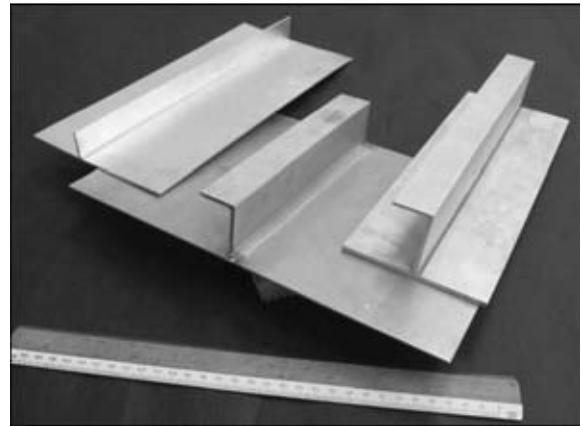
Фрагменты тонколистовых стрингерных панелей, изготовленных с выполнением электронно-лучевой сварки одно- и двухсторонних угловых швов
